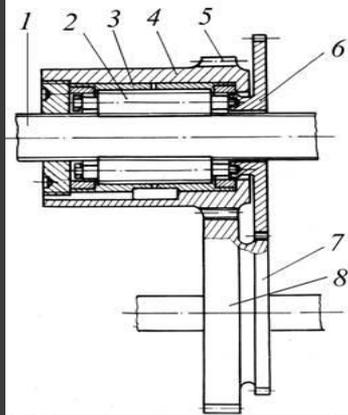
Передача с короткими резьбовыми роликами с дополнительными связями в виде зубчатых зацеплений: 1 – винт; 2 – ролик; 3 – гайка; 4 – корпус гайки; 5 – зубчатый венец корпуса; 6 – водило с зубчатым венцом; 7, 8 – венцы блока зубчатых колес
